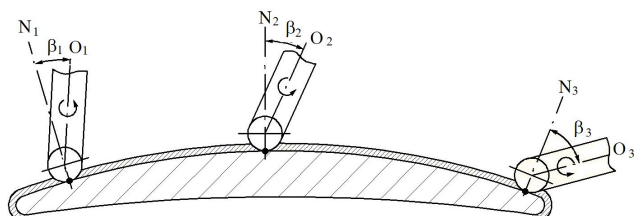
Положение инструмента на поверхности лопатки при токарном фрезеровании:
